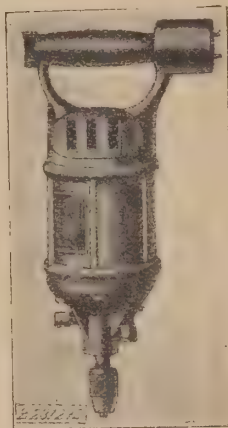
Handbohrmaschine mit Aluminiumgehäuse.
